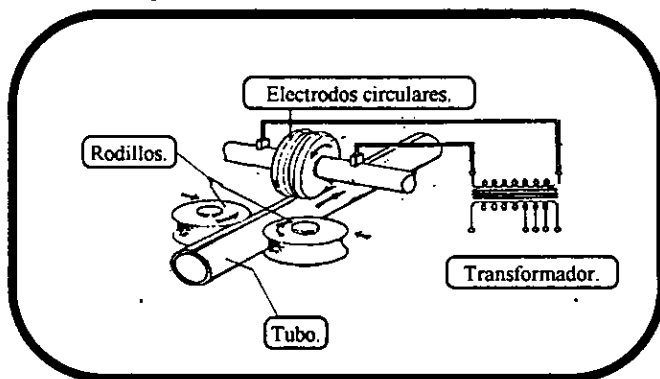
Soldadura por resistencia utilizando un equipo de baja frecuencia.(6)
